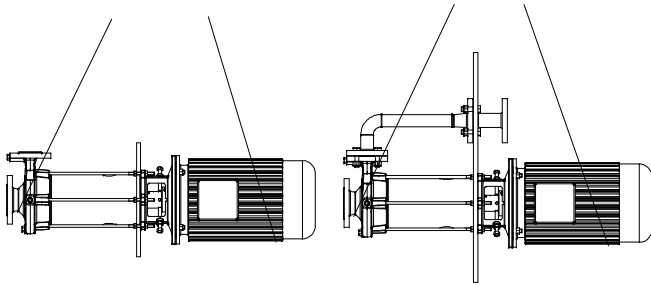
Как вариант - транспортировка агрегата без/с защитной плитой до типоразмеров 160 при больших глубинах установки ET
